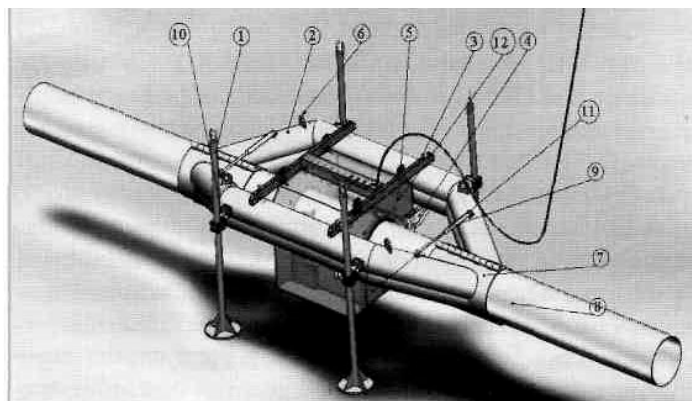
Общий вид подводного сварочного комплекса: опора – 1; установочная рама – 2; опорная балка – 3; откидной упор – 4; корпус кессона – 5; грузовая проушина – 6; трубный захват – 7; трубопровод – 8; гидронатяжитель – 9; герметизирующие створки – 10; камера для сухой сварки – 11; пневматическое уплотнение – 12
